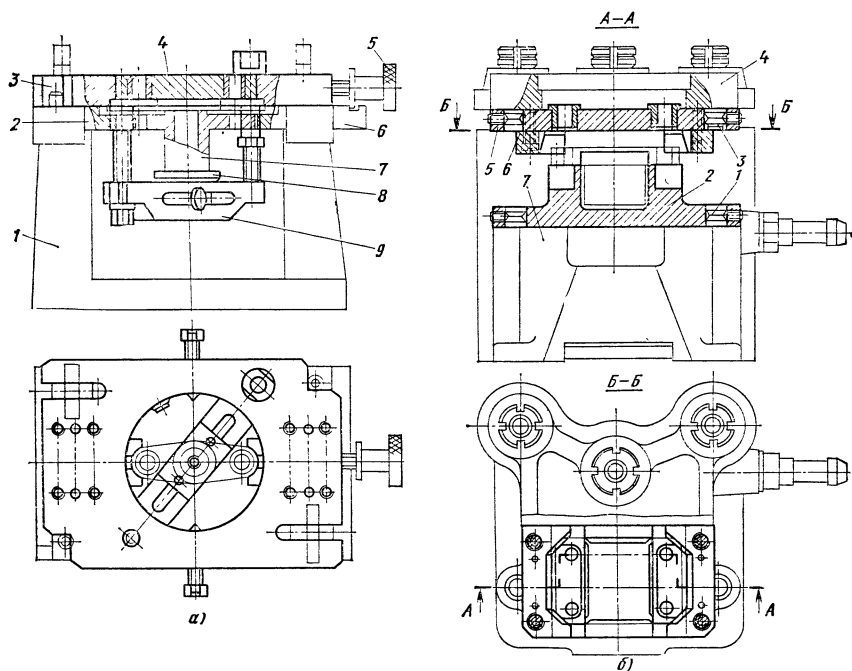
Компоновки, применяемые при сверлении отверстий во фланцах некруглой формы: а — накладного кондуктора; б — наладки скальчатого кондуктора
